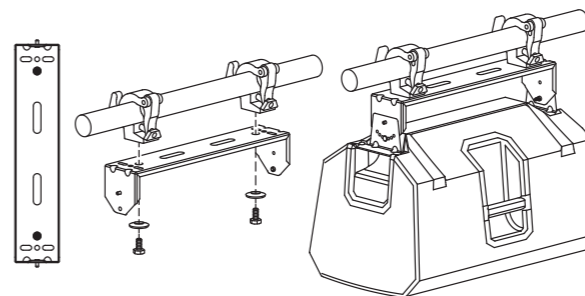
Montage horizontal à l'aide d'anneaux de levage TCA-1
